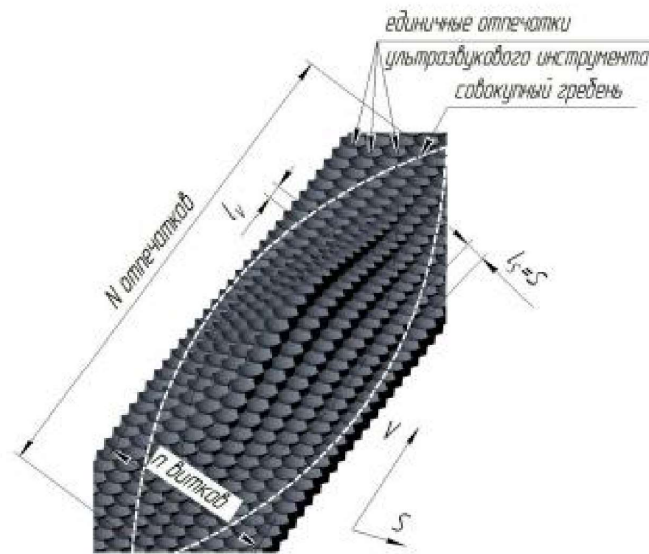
Схематическое изображение совокупного гребня волны при ударах инструмента
